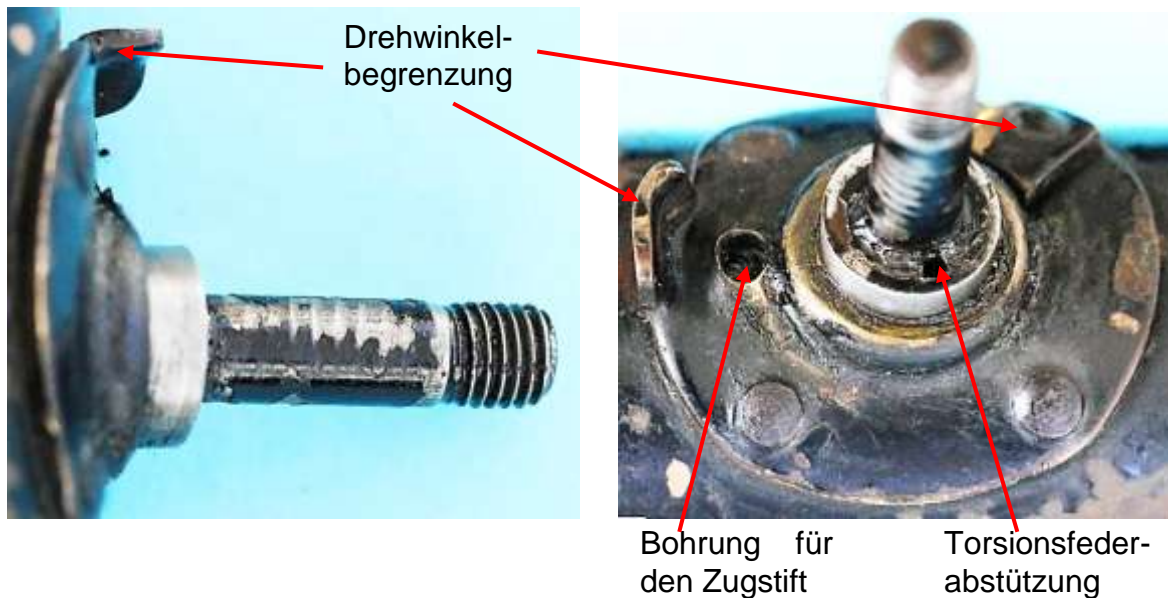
Kippvorrichtung: a) Drehbolzen mit angenietetem Flansch, b) Bohrungen für den Eingriff des Zugstifts und der Torsionsfeder
